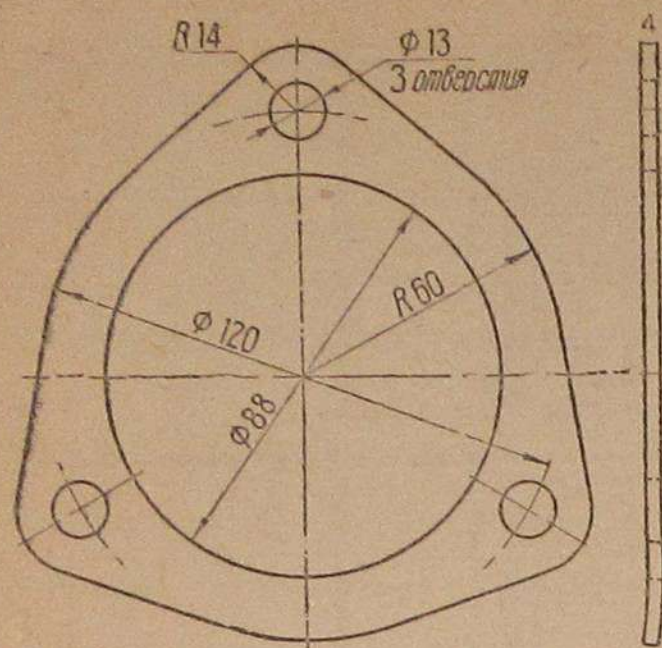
Прокладка фланца трубы отвода газа из газогенератора
